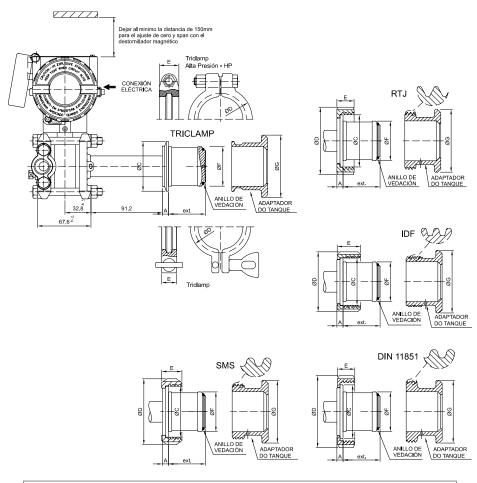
(e) – Diseño Dimensional de Montaje – Transmisor Sanitario sin Extensión
